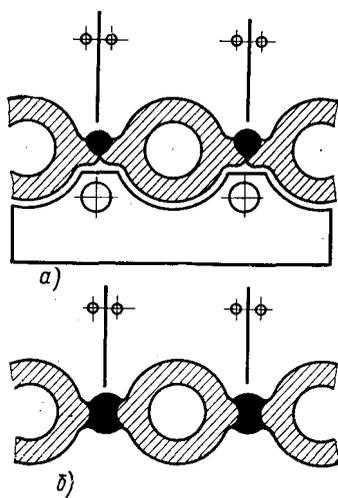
Сварка газоплотных панелей из плавниковых труб
